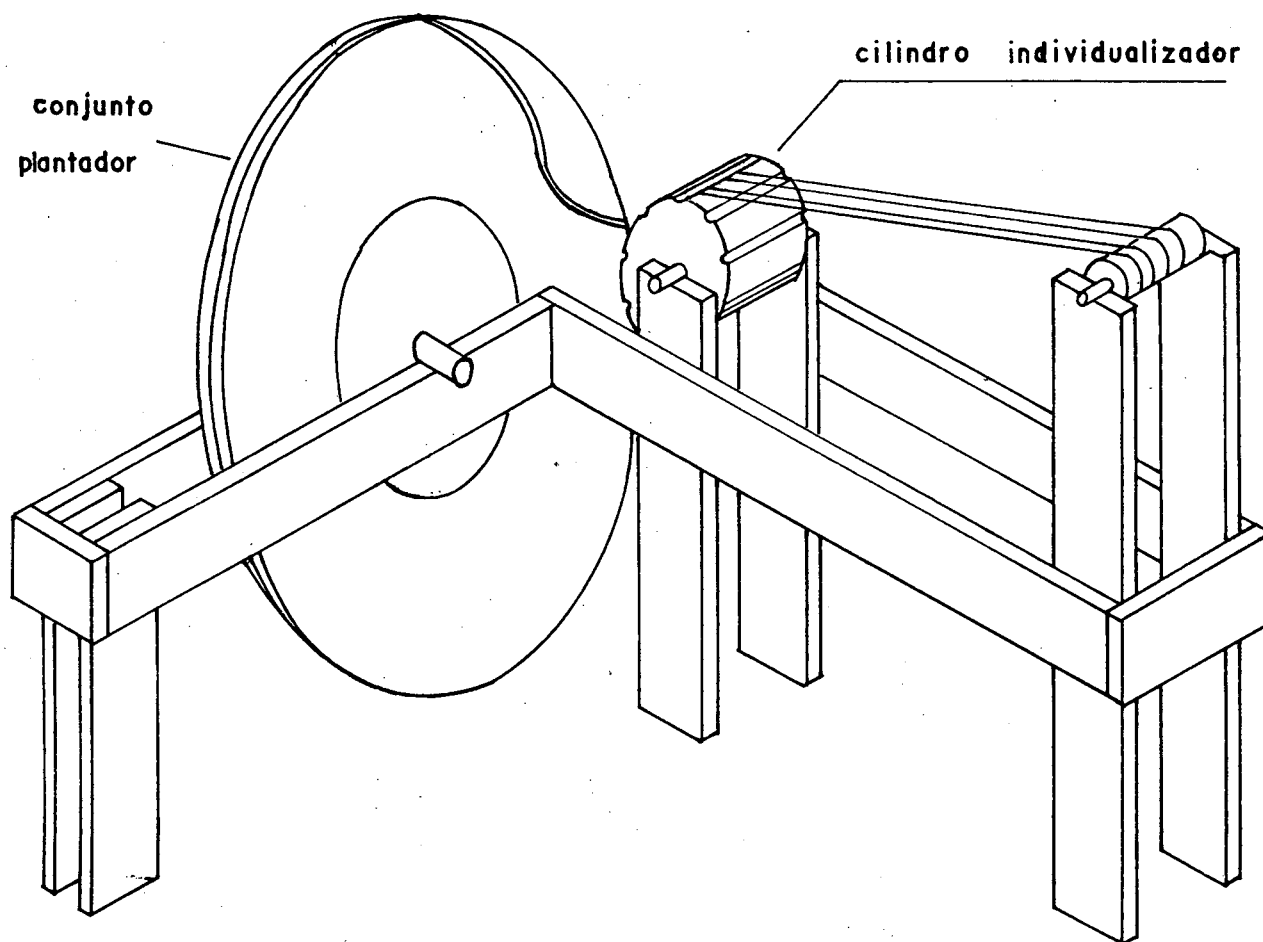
Esquema da montagem dos conjuntos alimentador e plantador.
